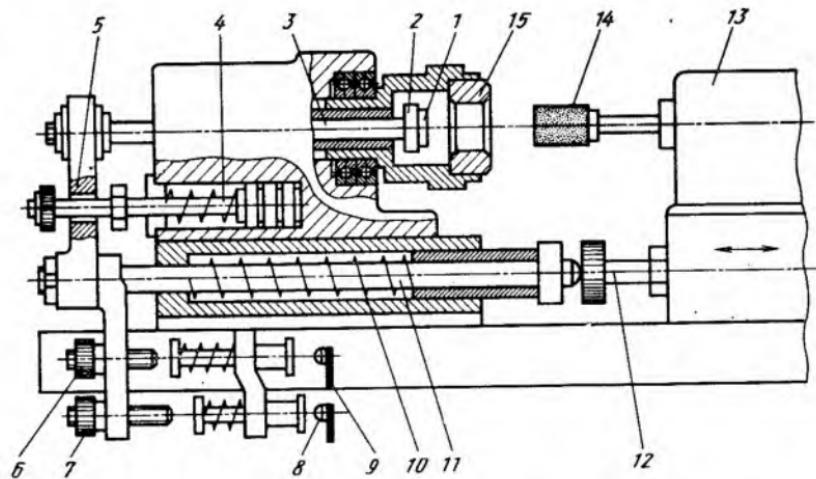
Схема подналадочной системы на бесцентрово-шлифовальном станке
